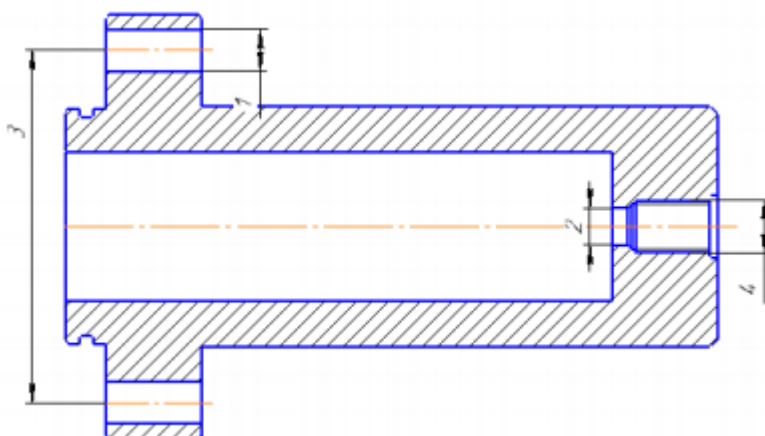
Креслення оброблюваної деталі з необхідними розмірами
